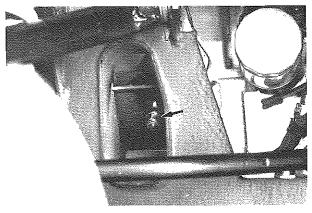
Viti di fissaggio laterale motore - Side engine screws
